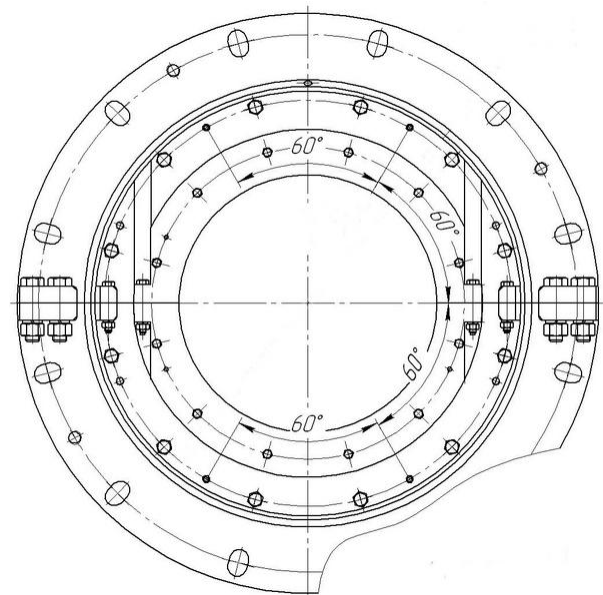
Герметизатор подшипникового узла. Вид спереди
